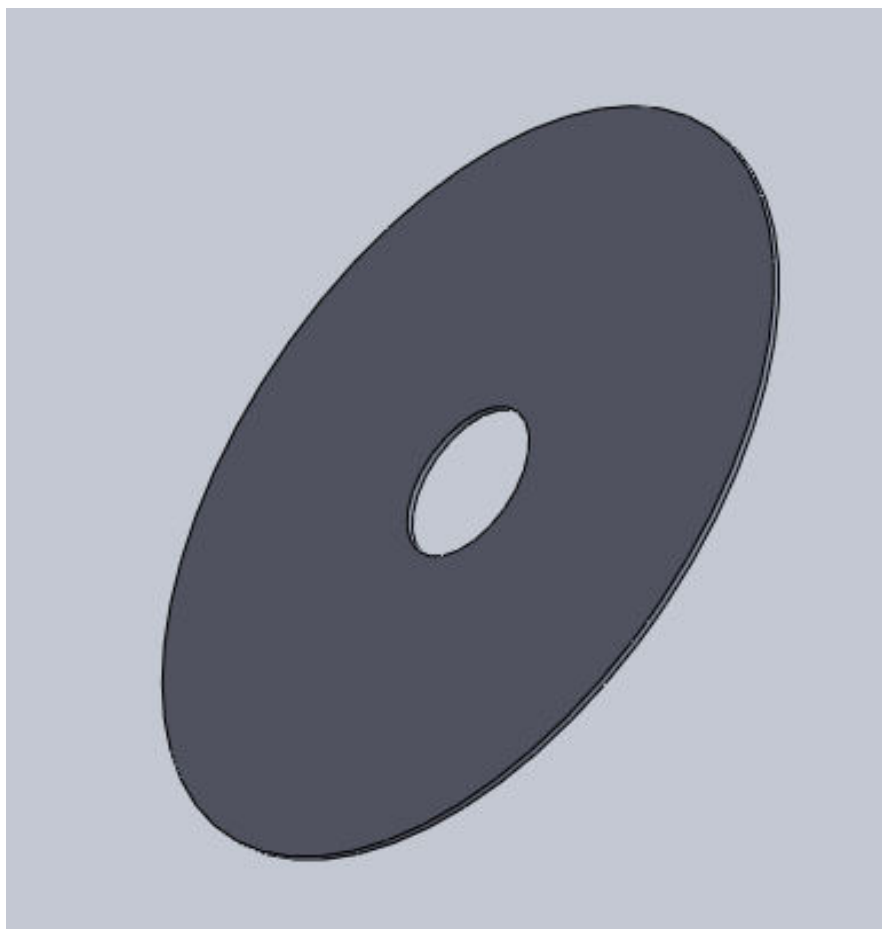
dimensionnement de disque par SOLIDWORKS
